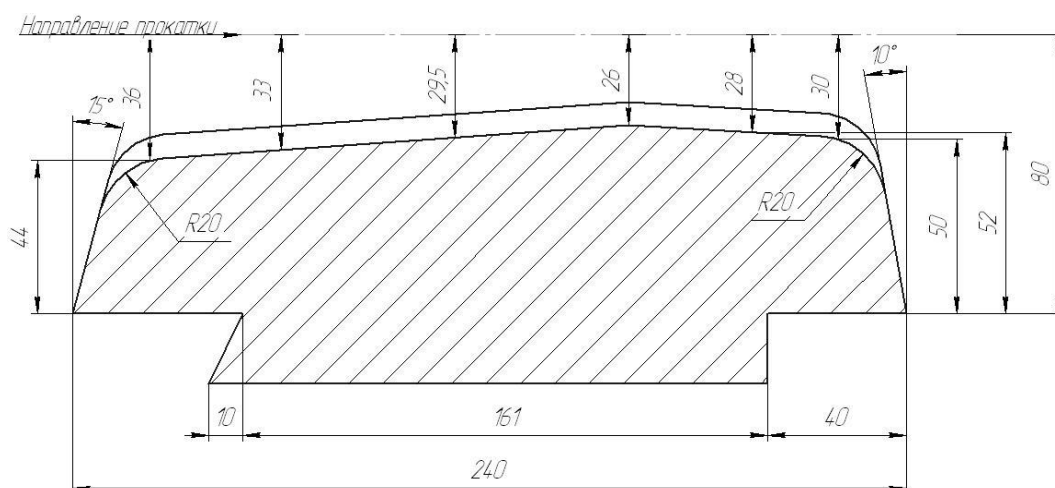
Калибровка линейки лабораторного стана «УралНИТИ» для исследования процесса риллингования с уменьшением диаметра трубы
